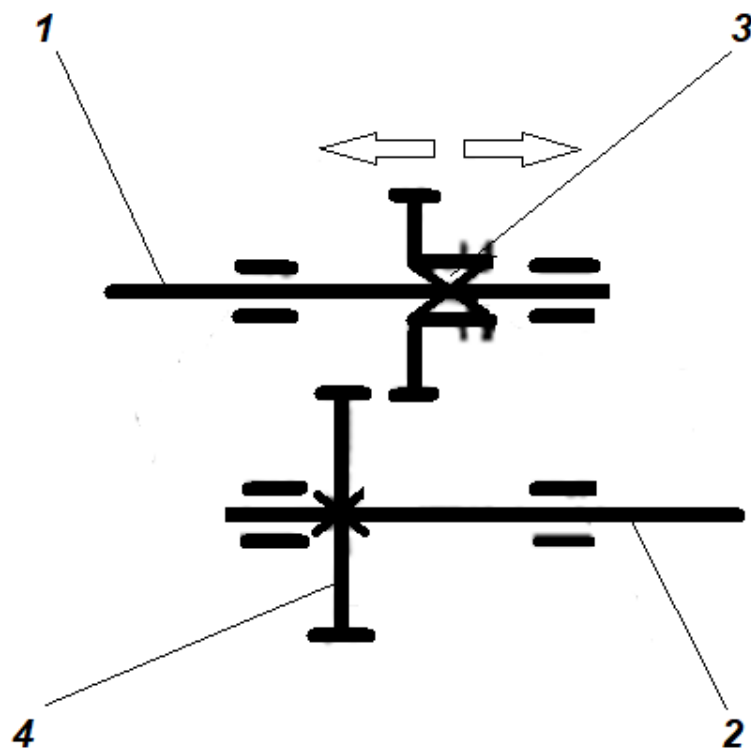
Принципова схема конструктивної реалізації коробки передач з рухомими зубчастими колесами (каретками) [40]:
